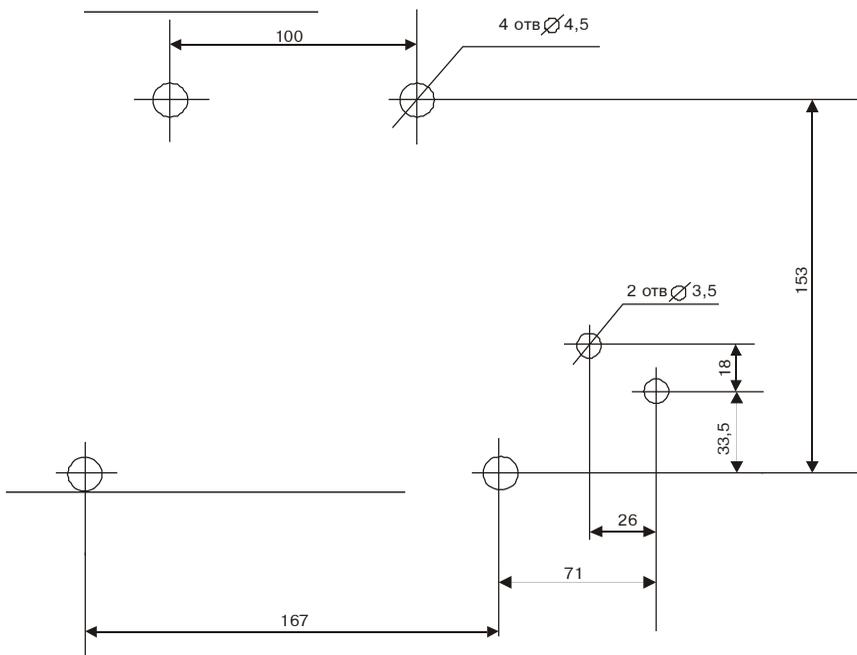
Схема разметки для установки БЦ-А исполнение 2
